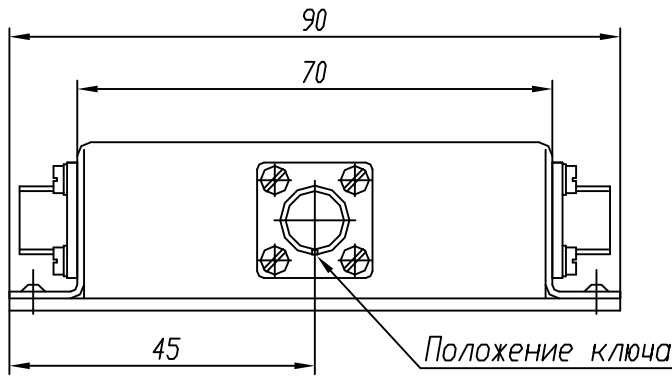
Габаритный чертеж коробки КСП2-3К-А
